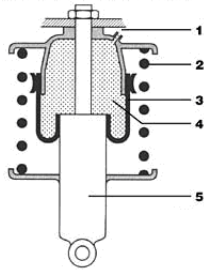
Конструкция пневмоэлемента пневматической подвески: 1 - воздушный штуцер; 2 - стальная пружина; 3 - пневмоэлемент; 4 - газовая камера; 5 - амортизатор.
